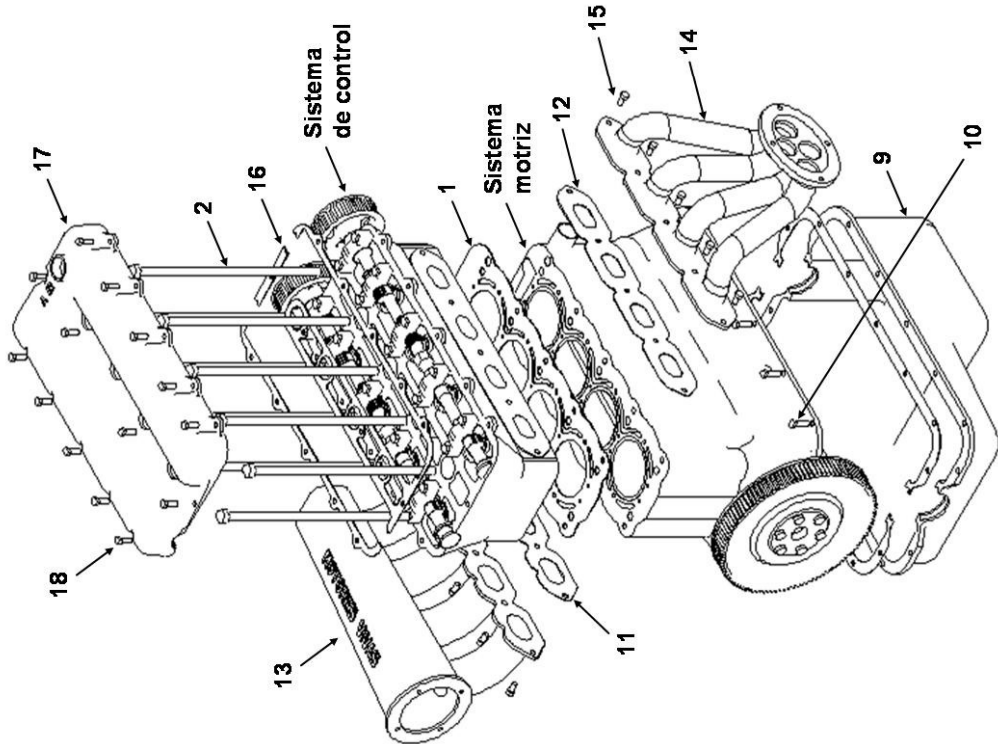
Despiece del diseño del motor a fabricar como prototipo
